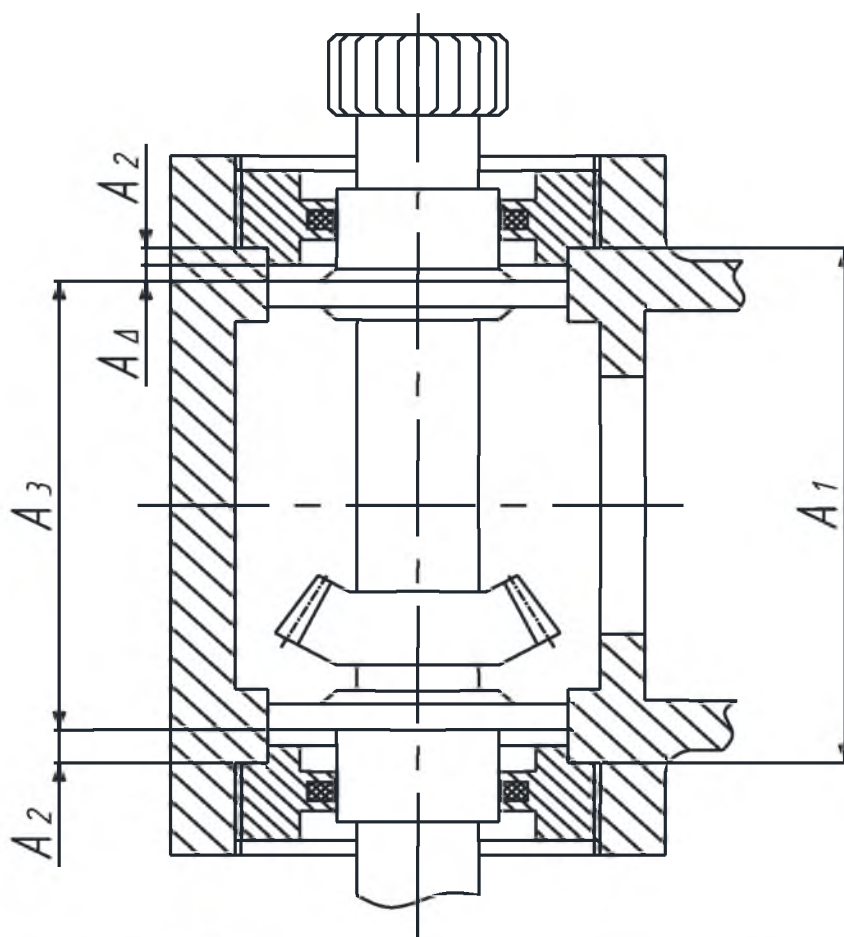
Эскиз узла редуктора винтового подъемника
